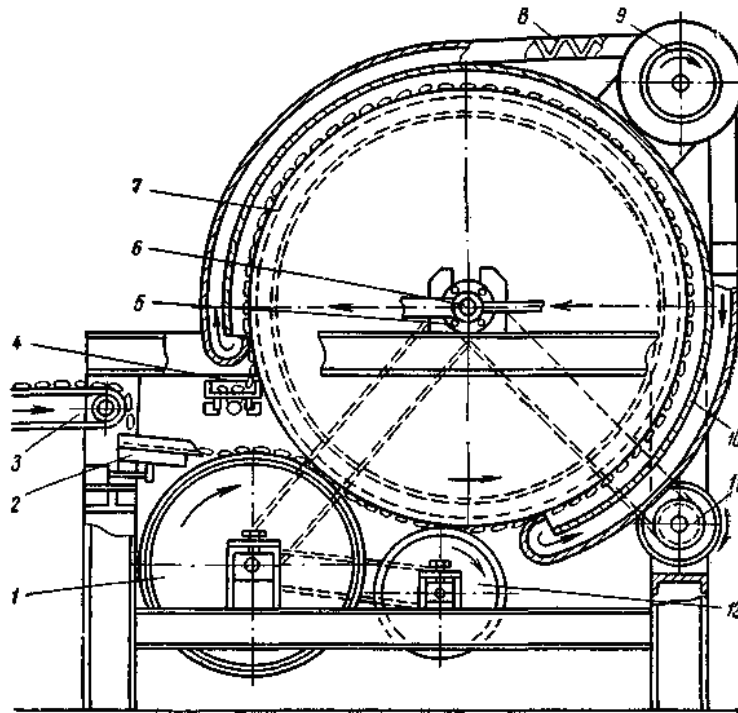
Морозильний апарат барабанного типу для заморожування вологих продуктів неправильної форми: 1 – живильний барабан; 2, 4 – вібрототики; 3 – вхідний конвеєр; 5 – підшипники; 6 – вал; 7 – заморожувальний барабан; 8 – повітроохолоджувач; 9 – вентилятор; 10 – кожух; 11 – електродвигун; 12 – прижимний барабан
